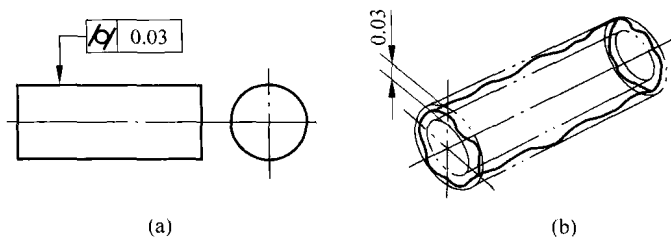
圆柱度公差的标注、公差带及测量方法
